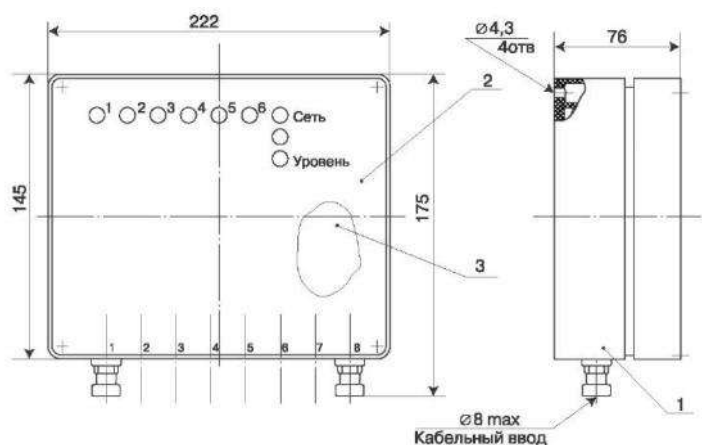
Габаритные и установочные размеры преобразователя передающего ППР-6, ППР-6И
